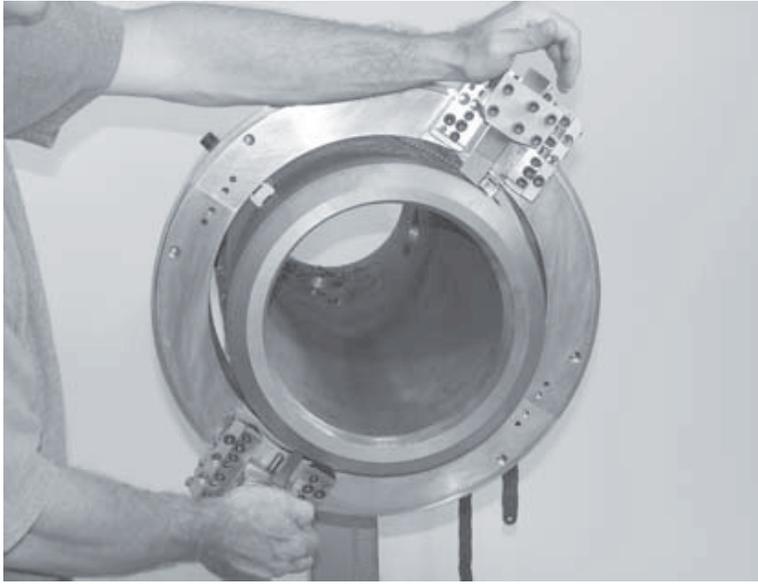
Ruotare la macchina per controllare il gioco dell'utensile.
